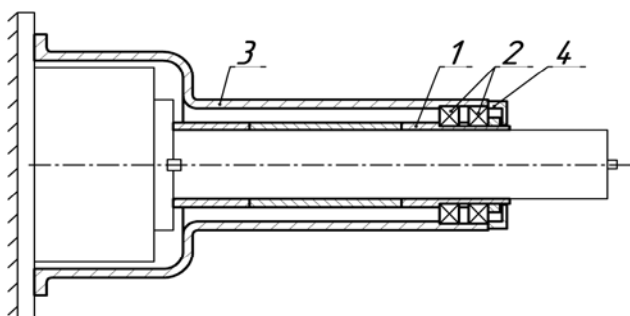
Принципиальная схема устройства для растачивания отверстий: 1 – сборная втулка; 2 – подшипники; 3 – корпус; 4 – крышка
